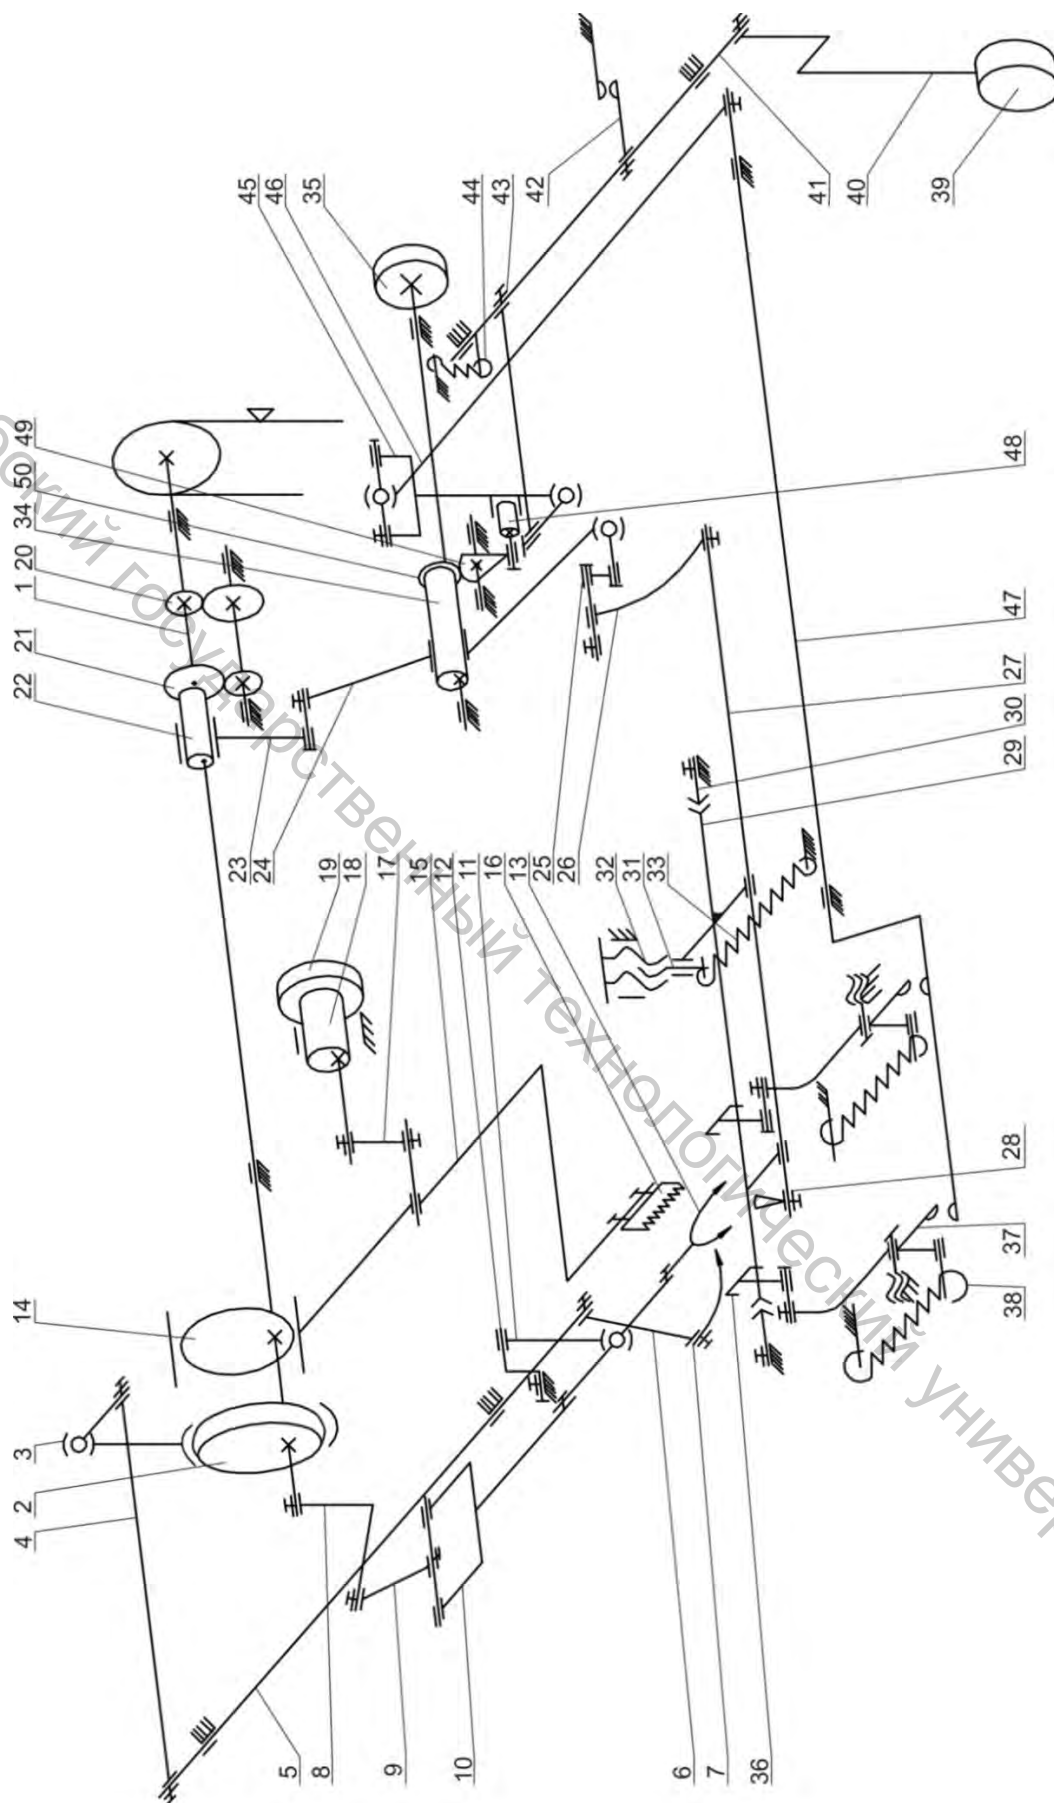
Кинематическая схема машины GL13101 Turpal
